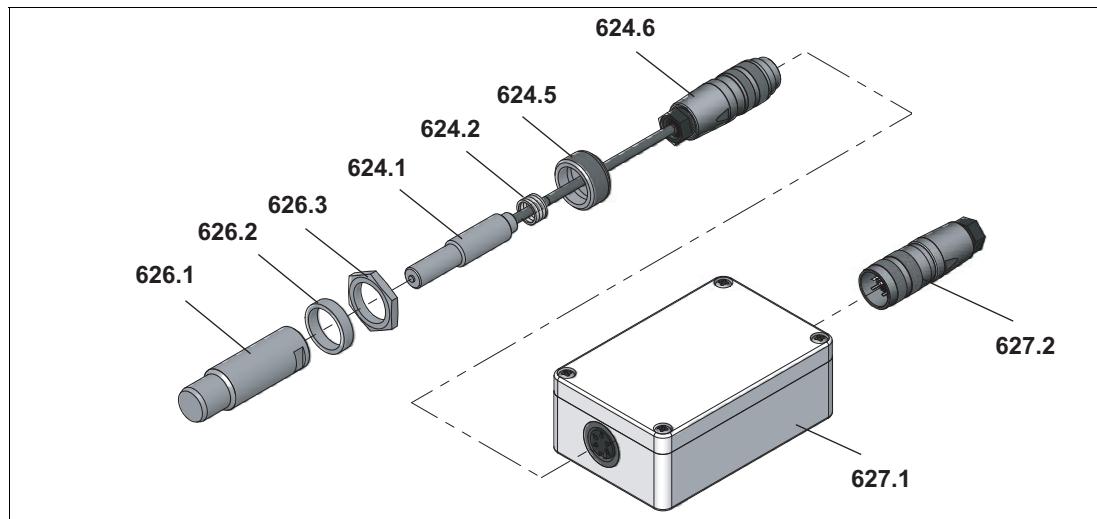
Übersichtszeichnung BEG 45 + BEV 13
